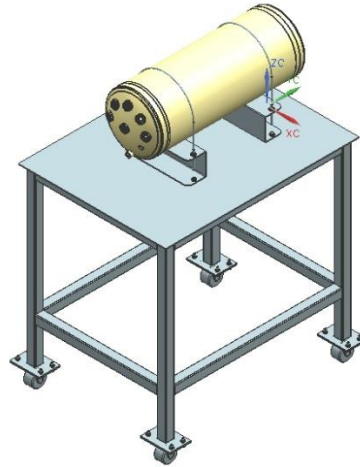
Vista Isométrica del Módulo 1 de la Mesa de Pruebas.
